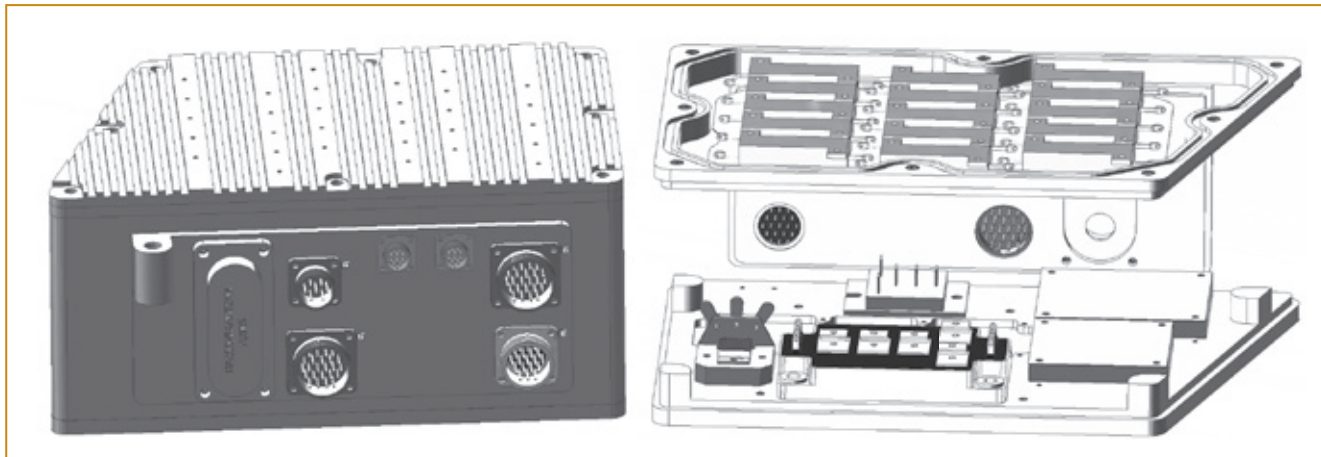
Внешний вид блока управления (справа вид блока управления без крышки радиатора и кожуха корпуса)
